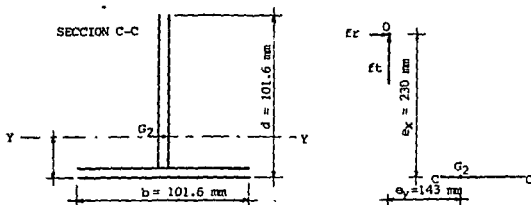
Dimensiones de la sección C-C de las soldaduras.
